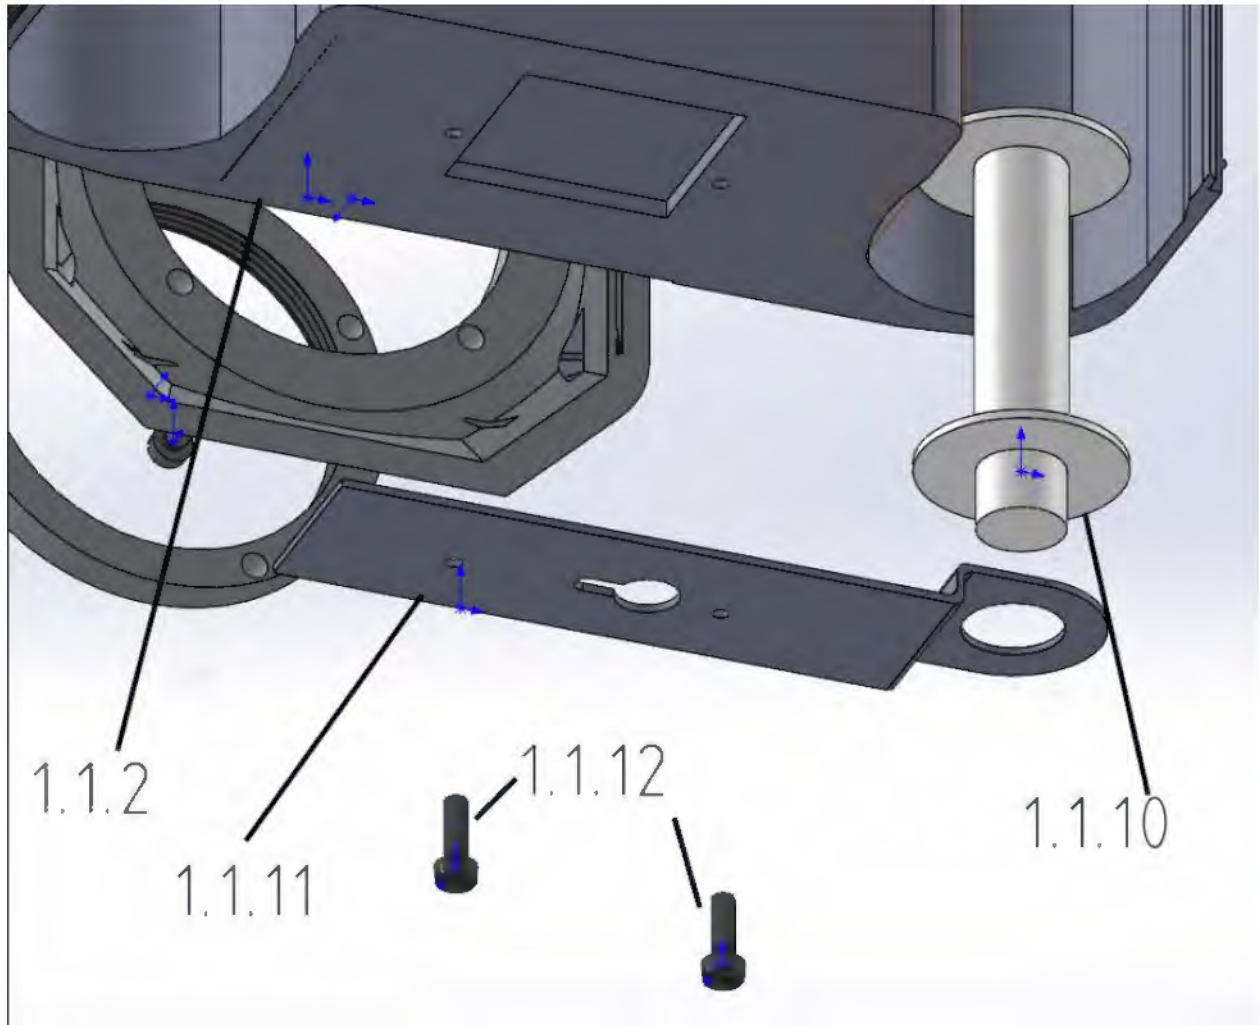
Demostración 3d de ensamblaje 1.1.11
